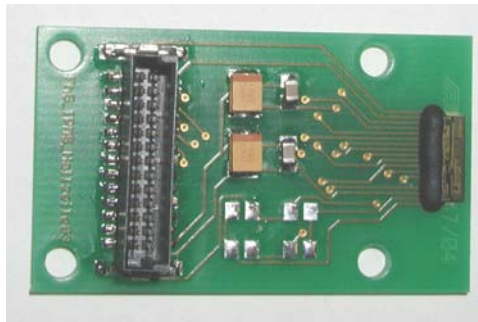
HLA32 montiert auf PCB (Evaluation-Board)
